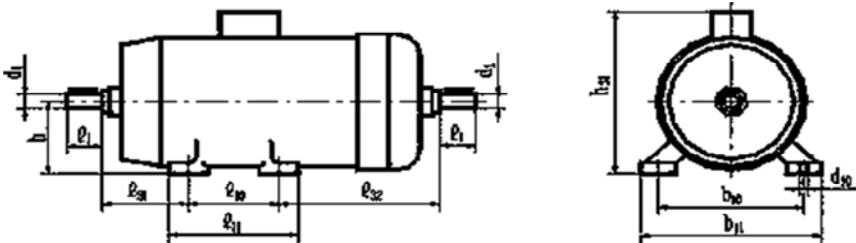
Габаритные и установочно-присоединительные размеры крановых двигателей
